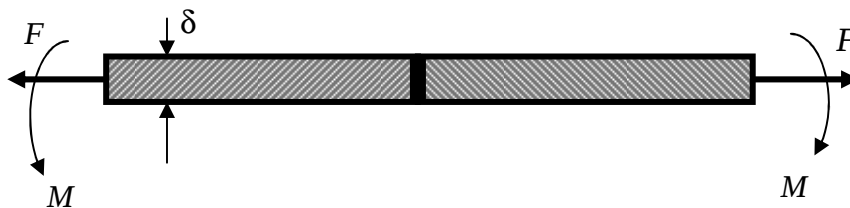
Схема нагружения сварного соединения встык
